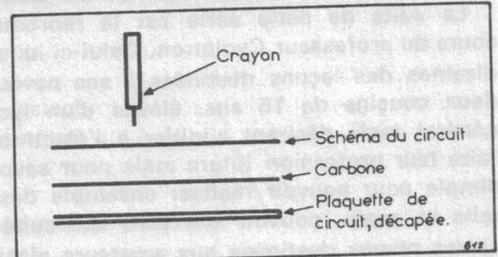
Pour reproduire sur la plaquette côté cuivre le dessin du circuit imprimé on intercale un papier carbone.
